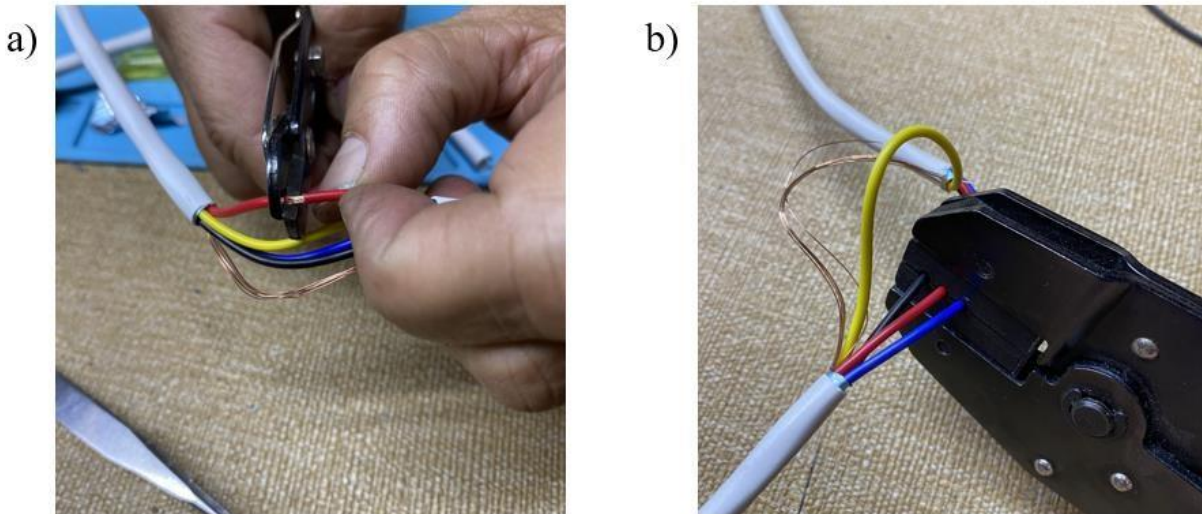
Corte de recubrimiento de cables a) herramienta convencional b) herramienta desarrollada en grupo HOH
